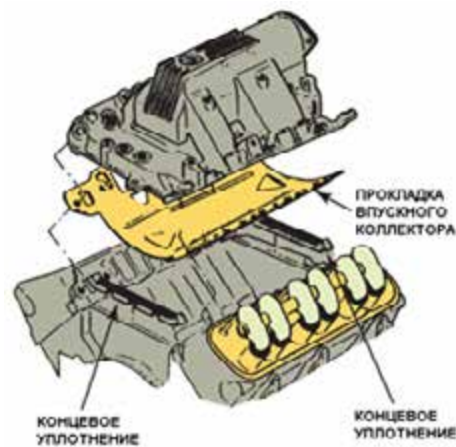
У этого впускного коллектора прокладка включает в себя торцевые уплотнения и полный защитный щиток для впадины, чтобы предотвратить нагрева впускной коллектор теплотой горячего двигателя и моторным маслом, которое омывает толкатели и кулачки распределительного вала; источник: *Pearson Education, Inc.
